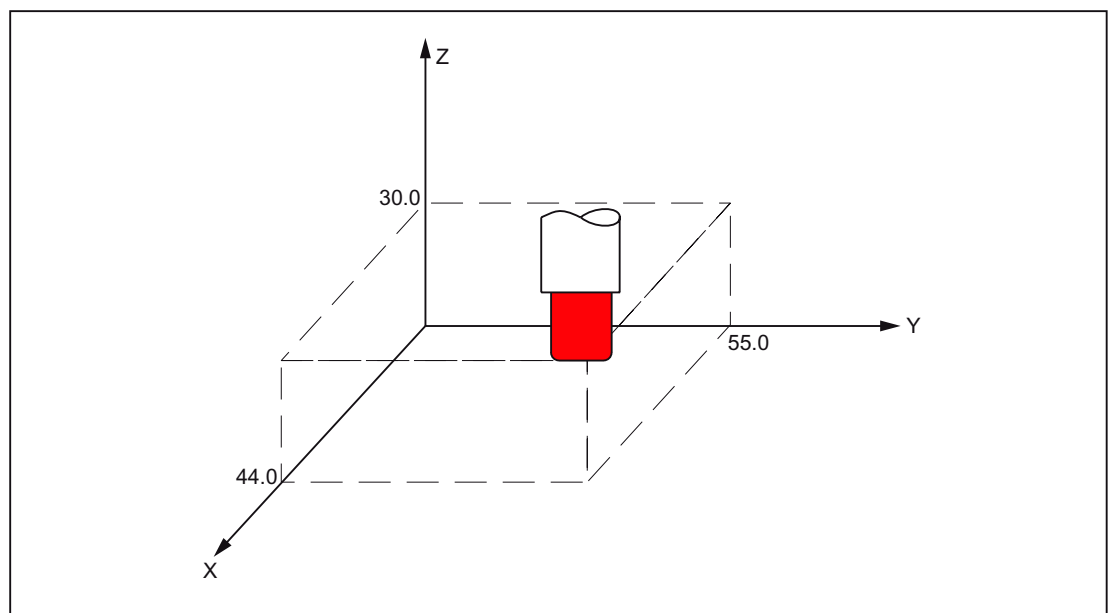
Mit X... Y... Z... angegebene Werkzeugposition
